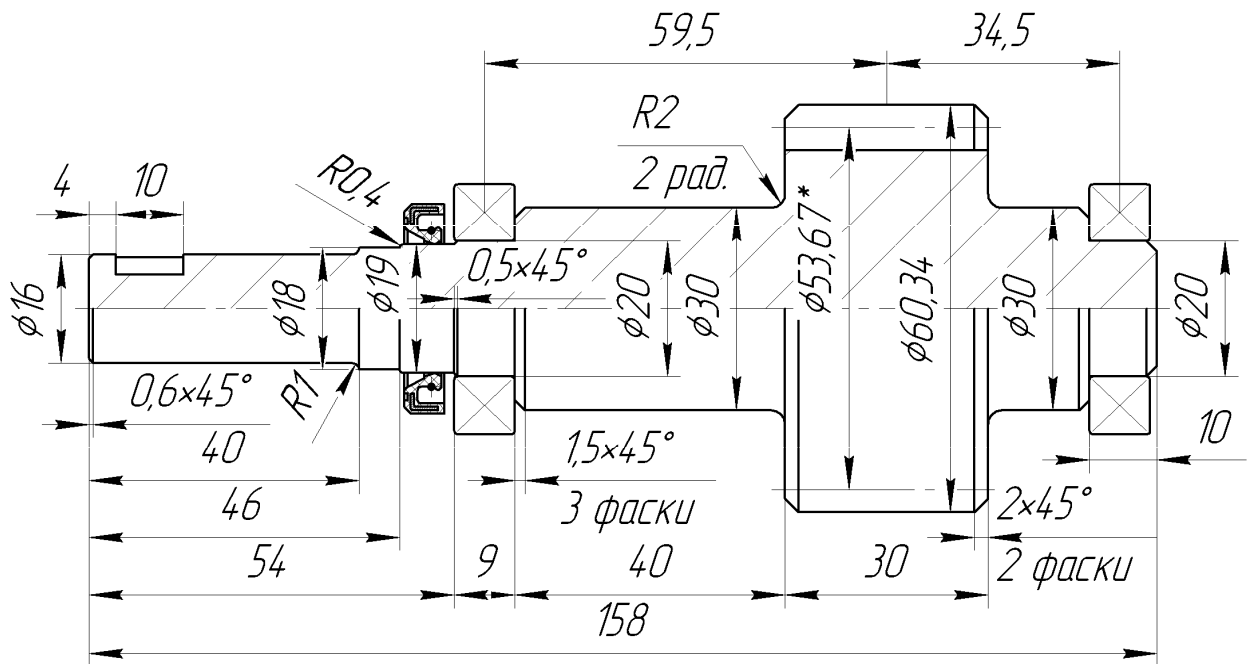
Компоновочно-расчетный эскиз вала (вал-шестерни)
